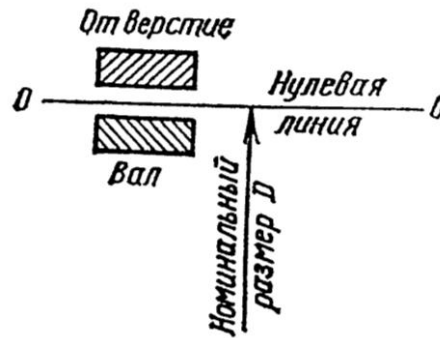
Поля допусков отверстия и вала при посадке с зазором
